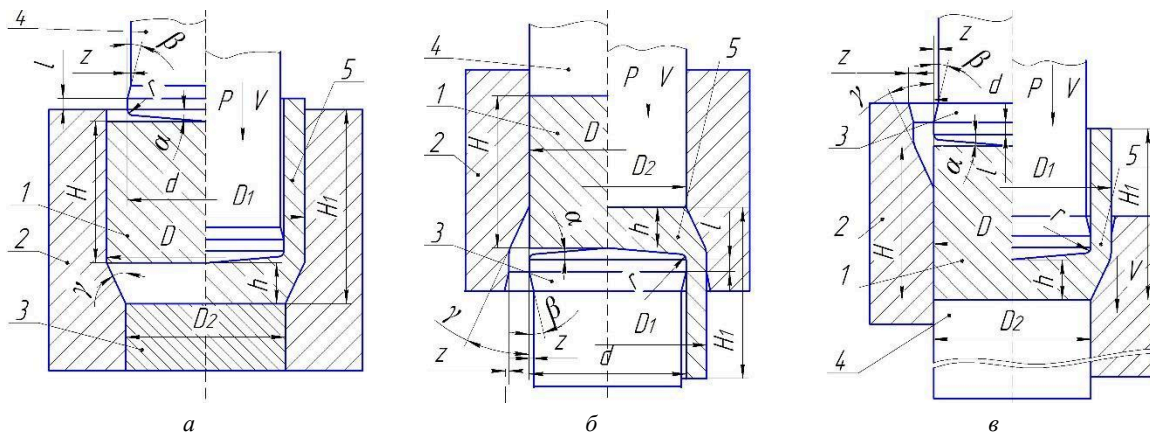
Схеми видавлювання порожнистих напівфабрикатів: а – схема зворотного видавлювання, б – схема прямого видавлювання з роздачою, в – схема зворотного видавлювання з роздачою
